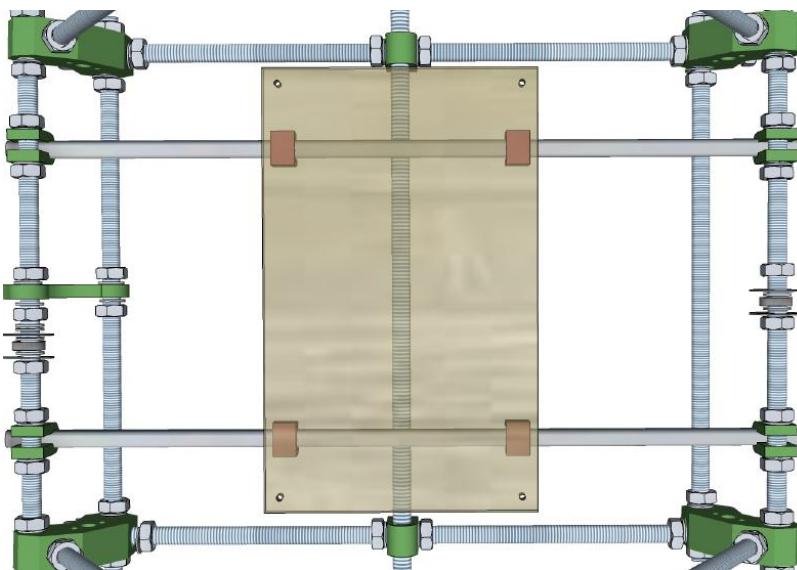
Colocación de varillas transversales y base de madera (paso 6)
